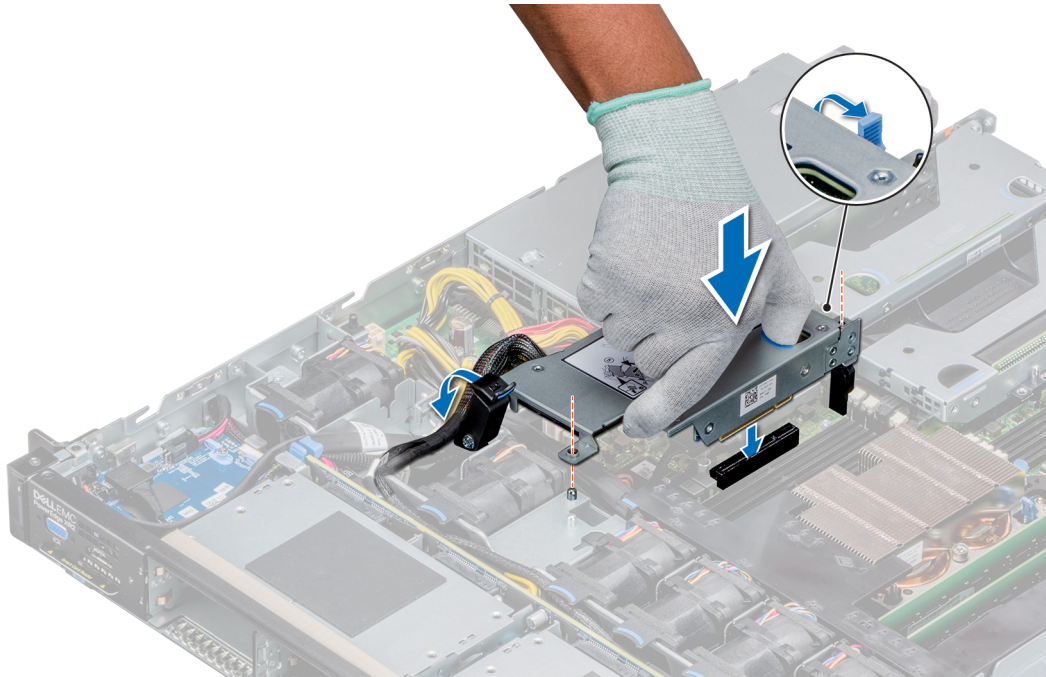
Instalación del soporte vertical para MiniPERC interna
